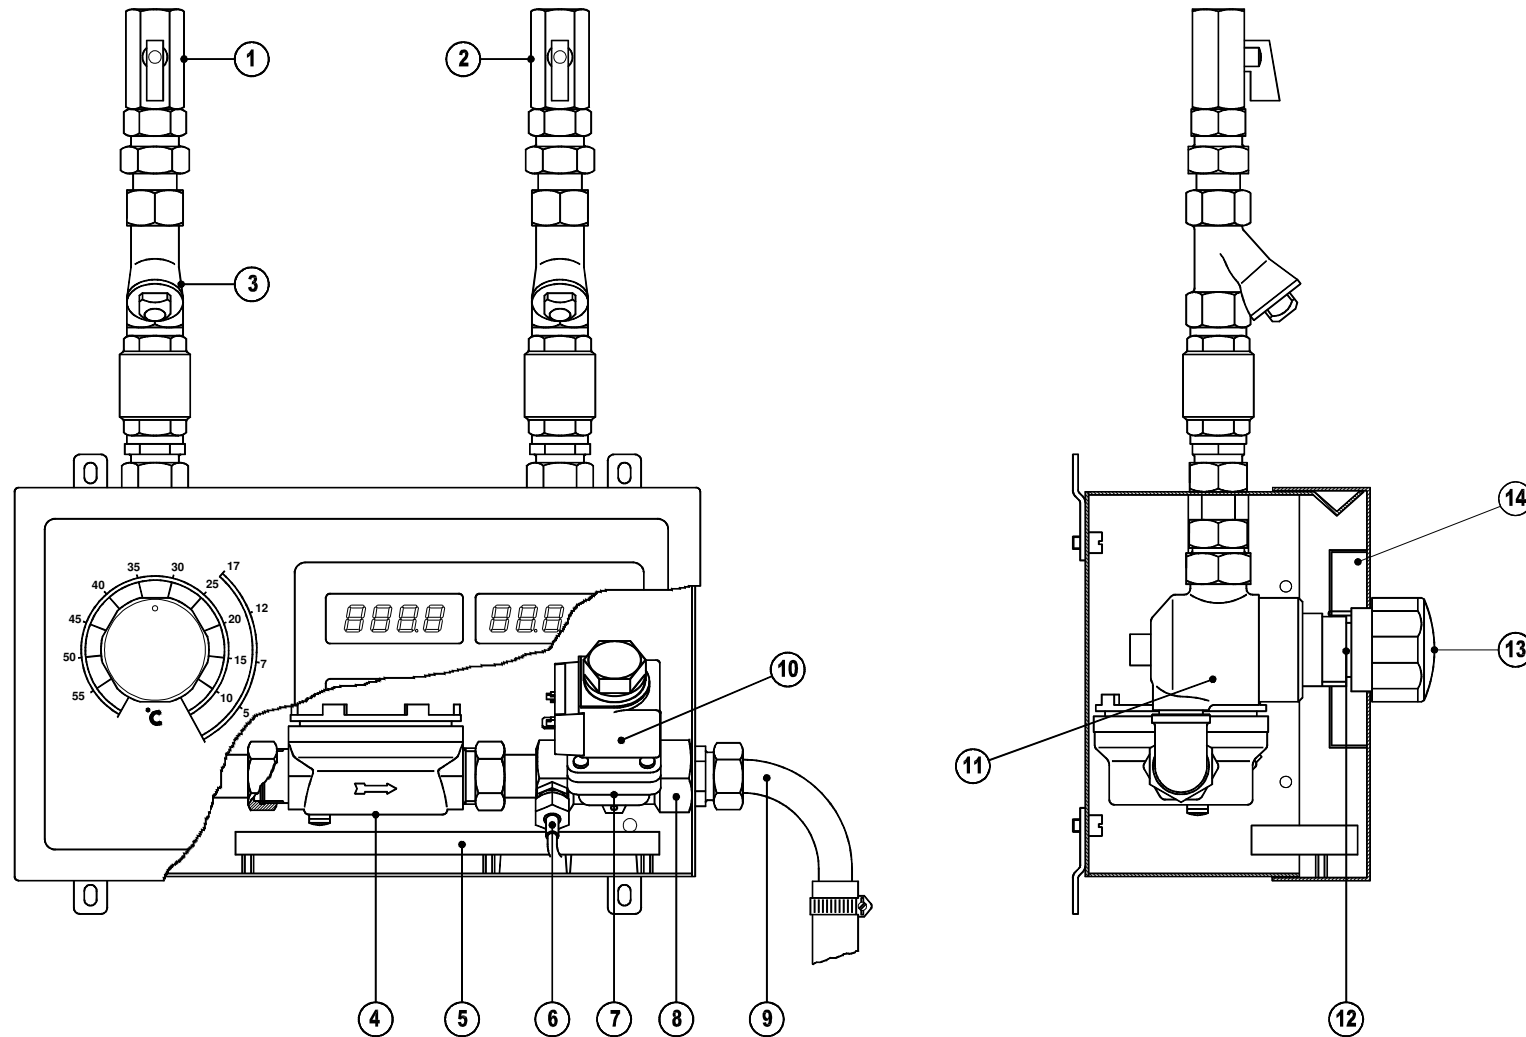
(Schema ricambi; Spare Parts scheme; Schéma des pièces détachées)
